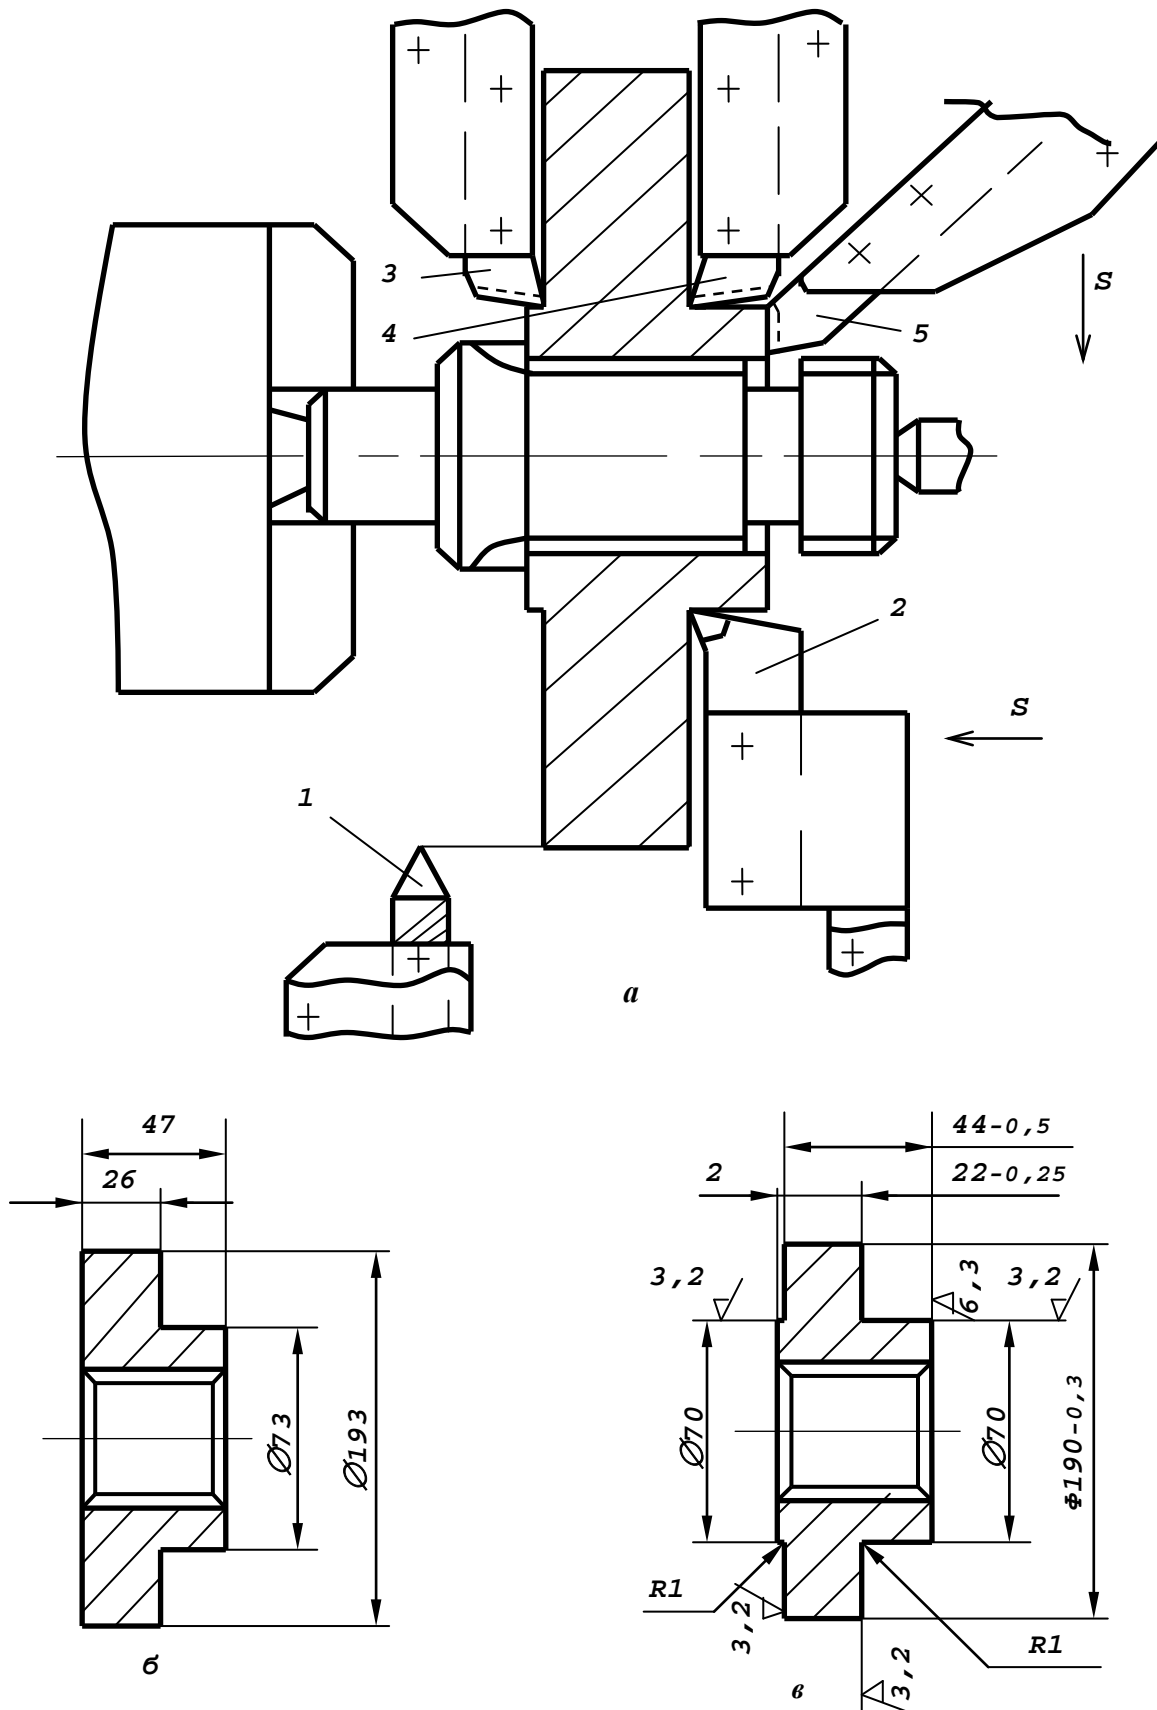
Эскиз наладки токарного одношпиндельного полуавтомата: а – наладка; б – колесо до обработки; в – колесо после обработки
